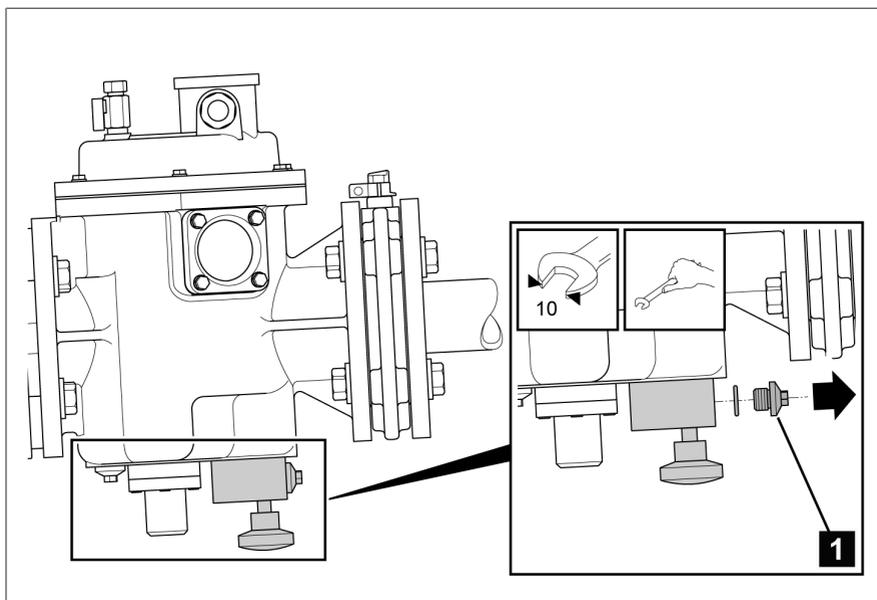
Rimuovere la vite nel blocco sul fondo dell'apparecchio (esempio bypass BPM)
